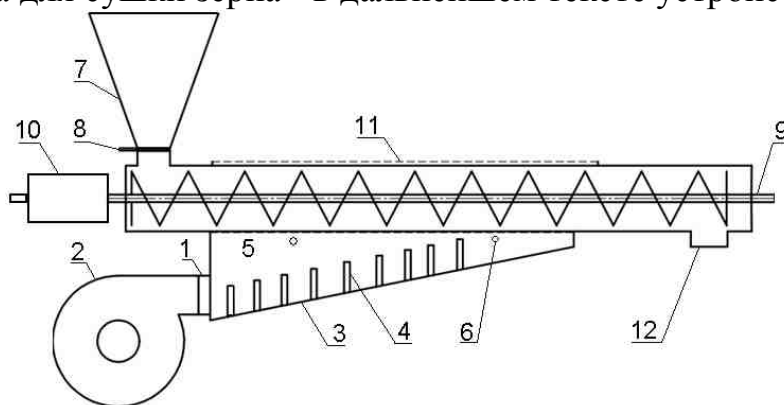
Общий вид шнекового устройства для сушки зерна.
